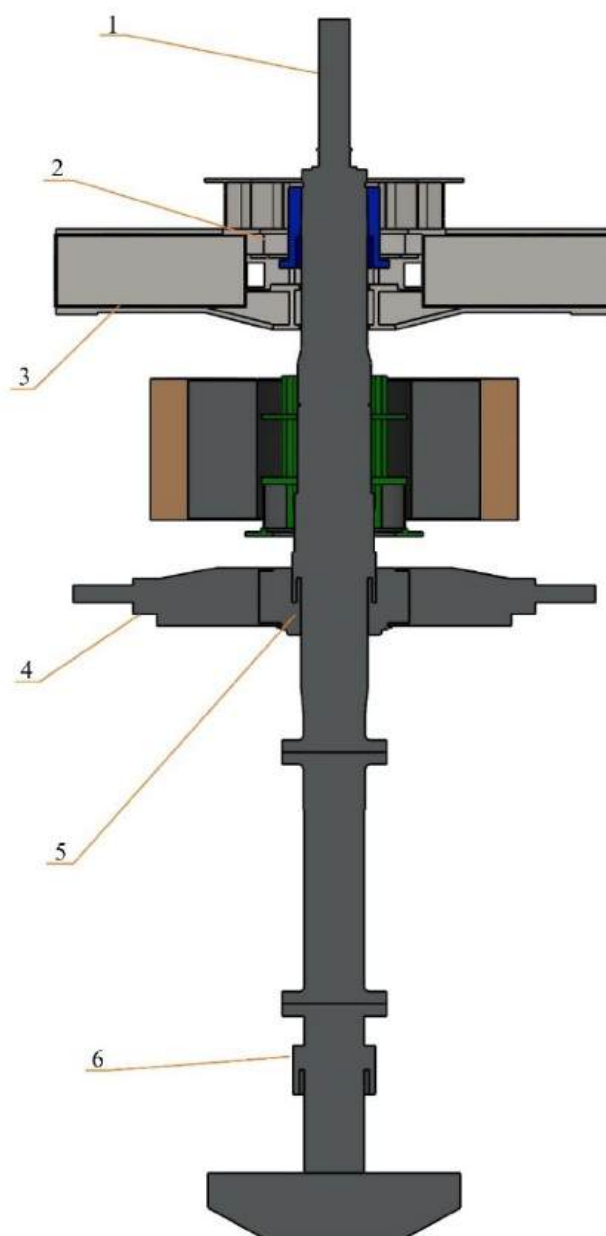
Тривимірний модель конструкції існуючого гідрогенератора-двигуна у поперечному розрізі (1 – розгінний двигун, 2 – верхній генераторний підшипник, 3 – верхня хрестовина, 4 – нижня хрестовина, 5 – нижній генераторний підшипник, 6 – турбінний підшипник)
